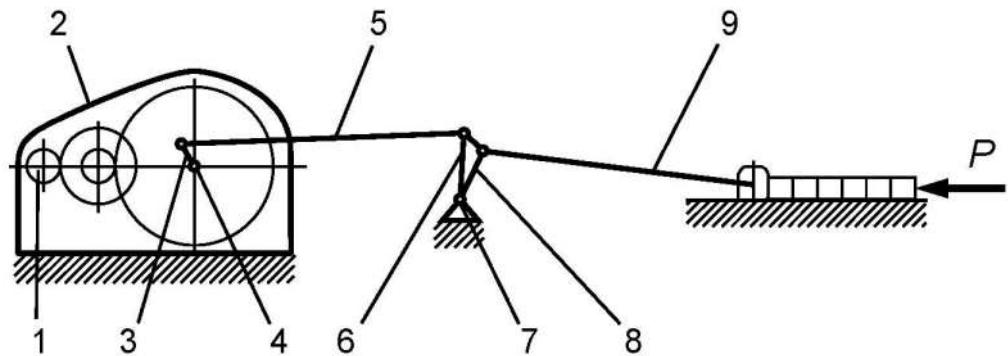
Схема рычажного толкателя: 1 - входной вал; 2 - редуктор; 3 - кривошип; 4 - выходной вал; 5 - шатун; 6 - рычаг; 7 - вал; 8 - короткие рычаги; 9 - толкающие штанги
